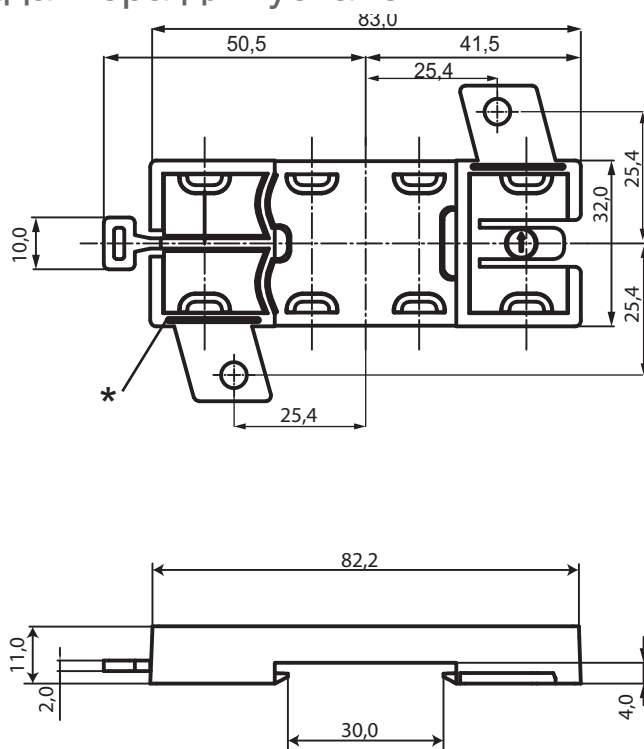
Чертеж с указанием размеров адаптера для установки
